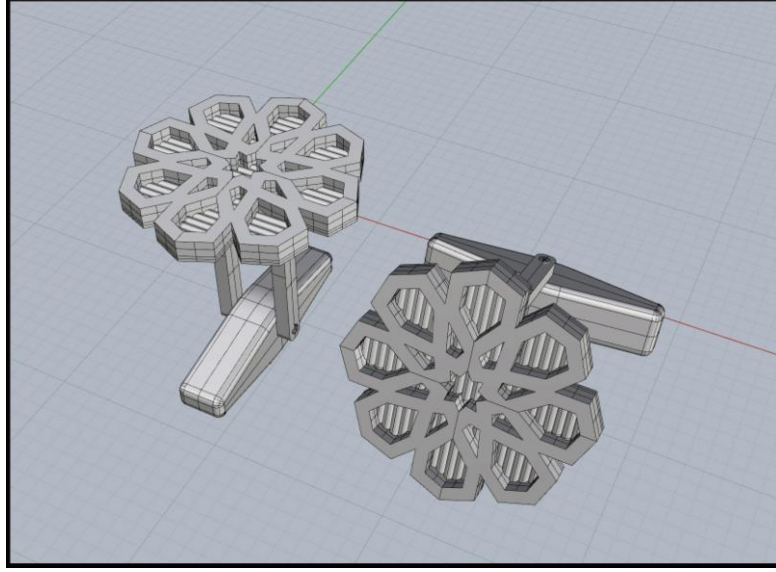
Kol düğmesinin Vray motoru ile görselleştirilmesi
